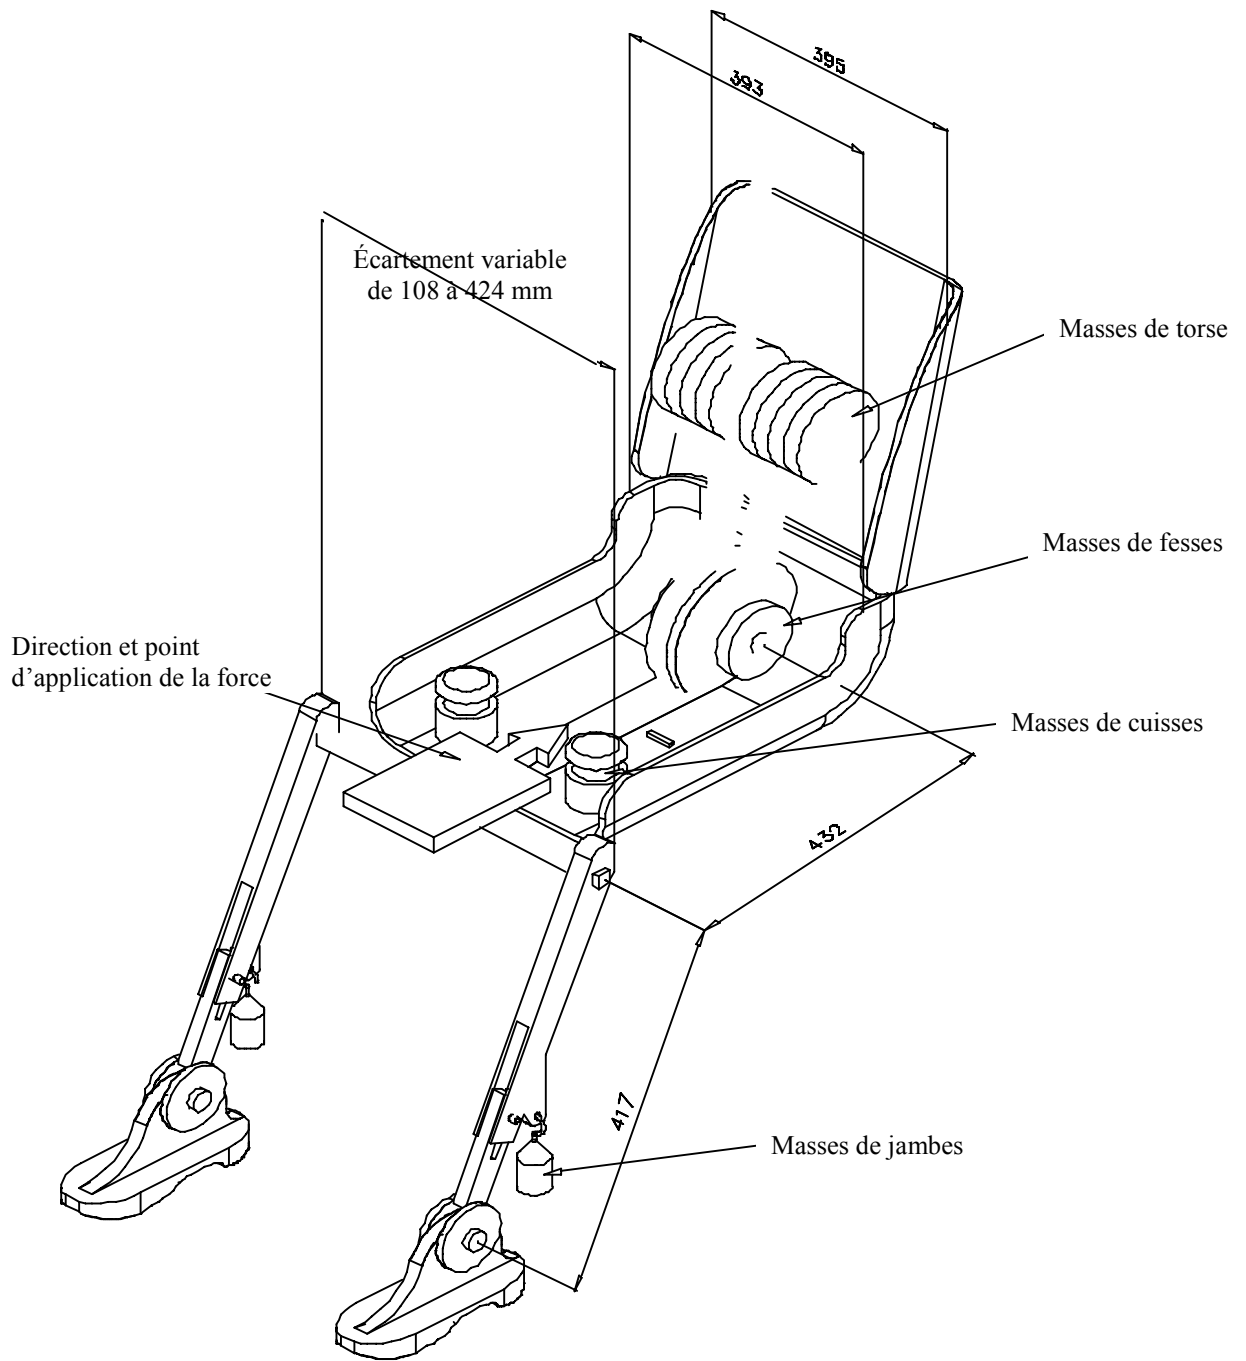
Dimensions des éléments de la machine 3 DH et emplacement des masses
